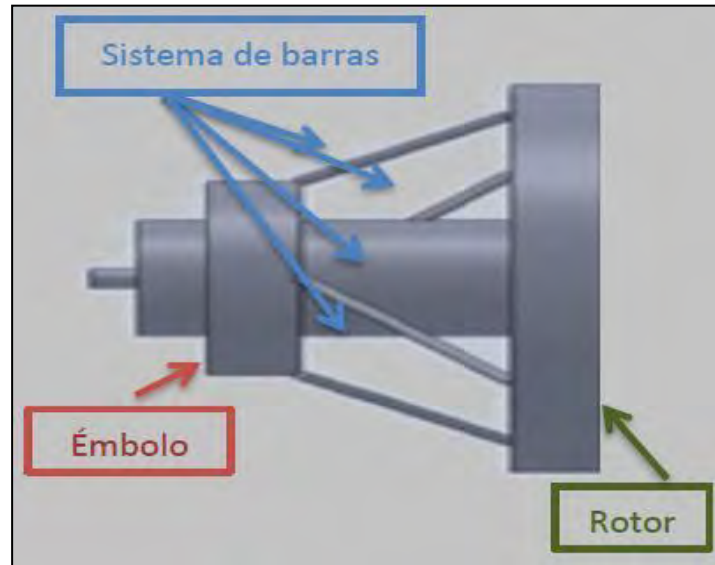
Diseño del actuador de doble efecto rotativo.
